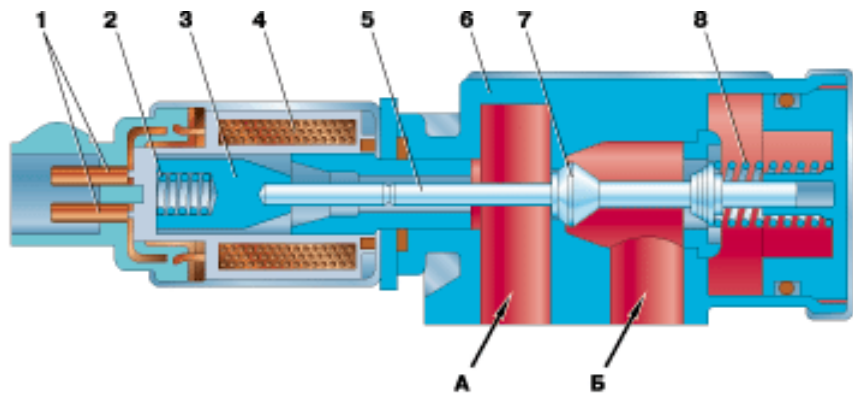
Регулятор холостого хода двигателя F3R 272: 1 – штекерные выводы обмотки электромагнита; 2 – демпфирующая пружина; 3 – сердечник; 4 – обмотка электромагнита; 5 – толкатель; 6 – корпус регулятора; 7 – упор клапана; 8 – возвратная пружина; А – канал забора дополнительного воздуха; Б – канал подачи дополнительного воздуха во впускную трубу
